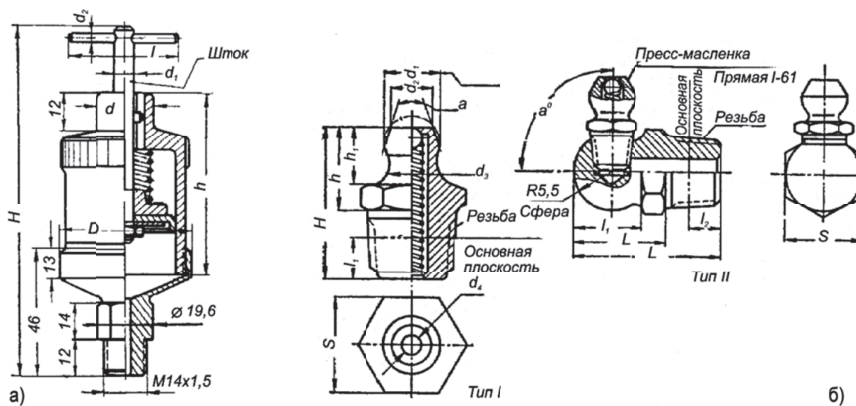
Масленка для принудительной подачи смазки (а) и пресс-масленка для смазки (б)
